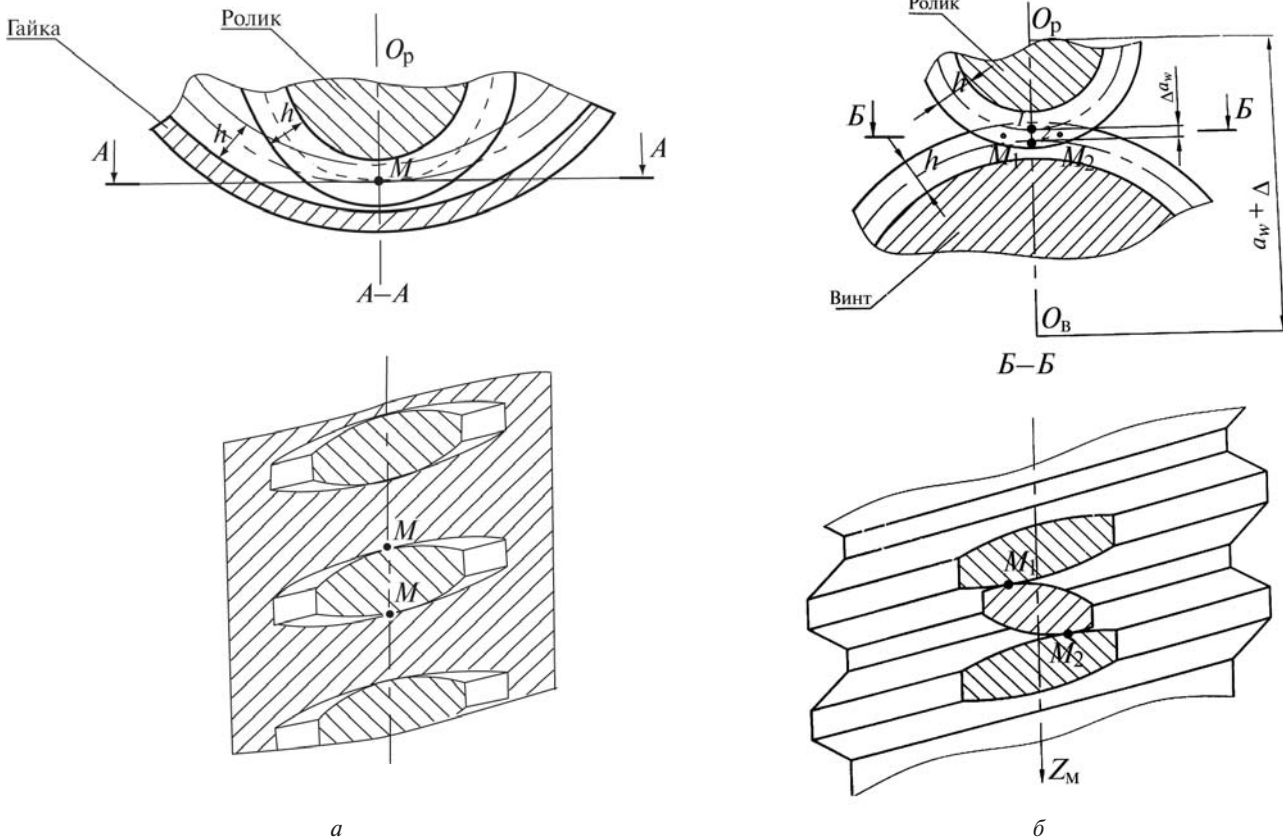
Характер сопряжения витков резьбы: а — ролика и гайки; б — ролика и винта
